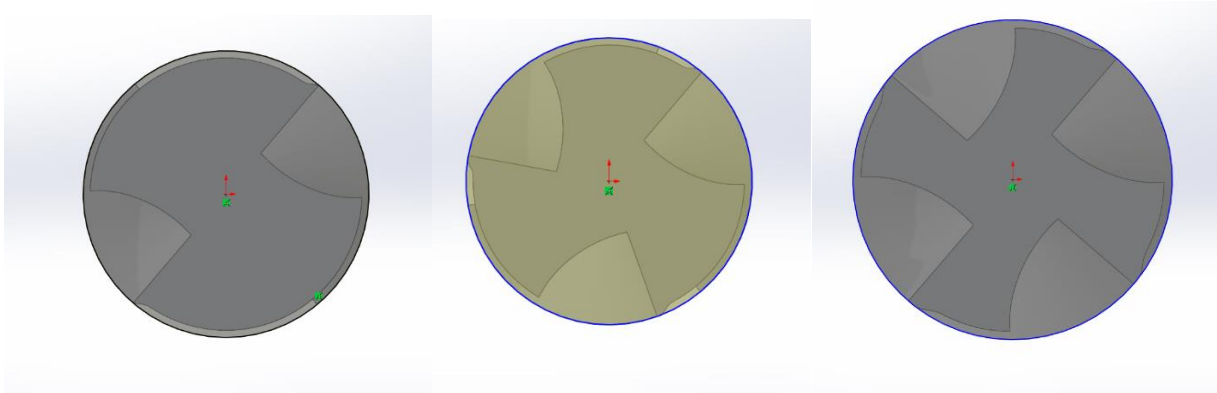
Περιστροφή για δημιουργία ελίκωσης
